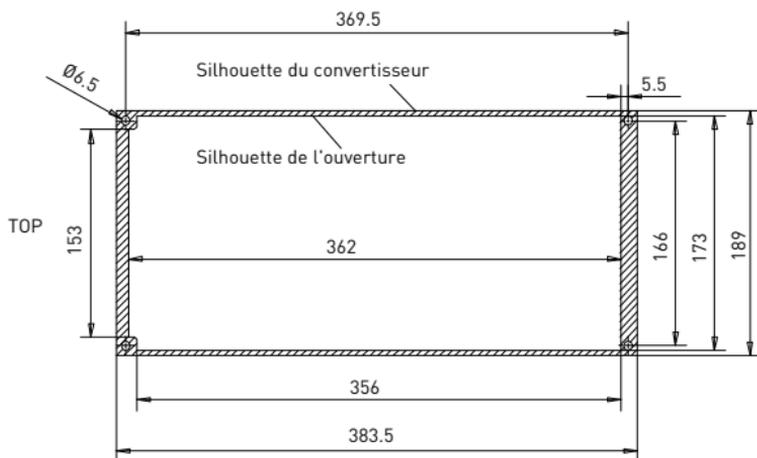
dimensions de découpe en montage par bride, pour MI4 (unité: mm)
